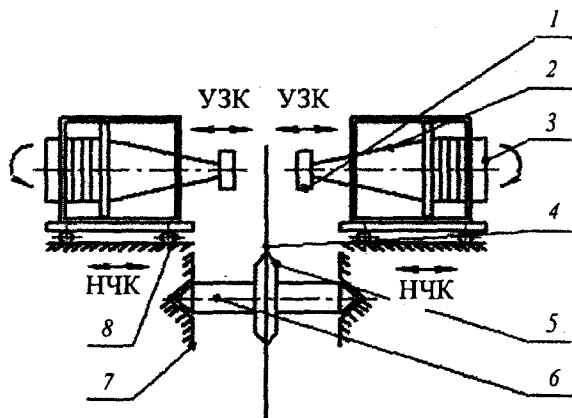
Схема установки для шаржирования распиловочных дисков с использованием совместного действия низкочастотной и ультразвуковой составляющих колебаний при жестком закреплении заготовки
